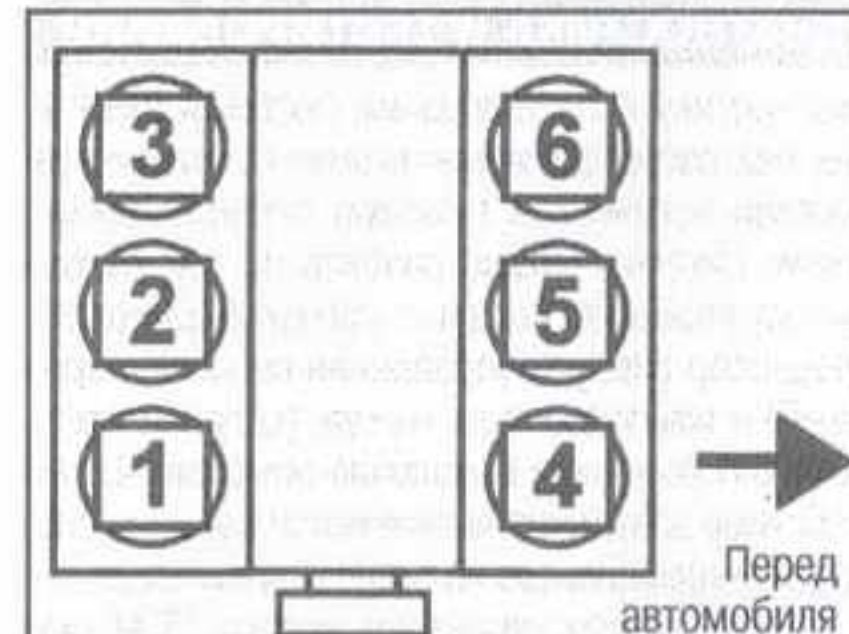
Порядок работы цилиндров двигателя V6 3,5 л: 1-4-2-5-3-6
